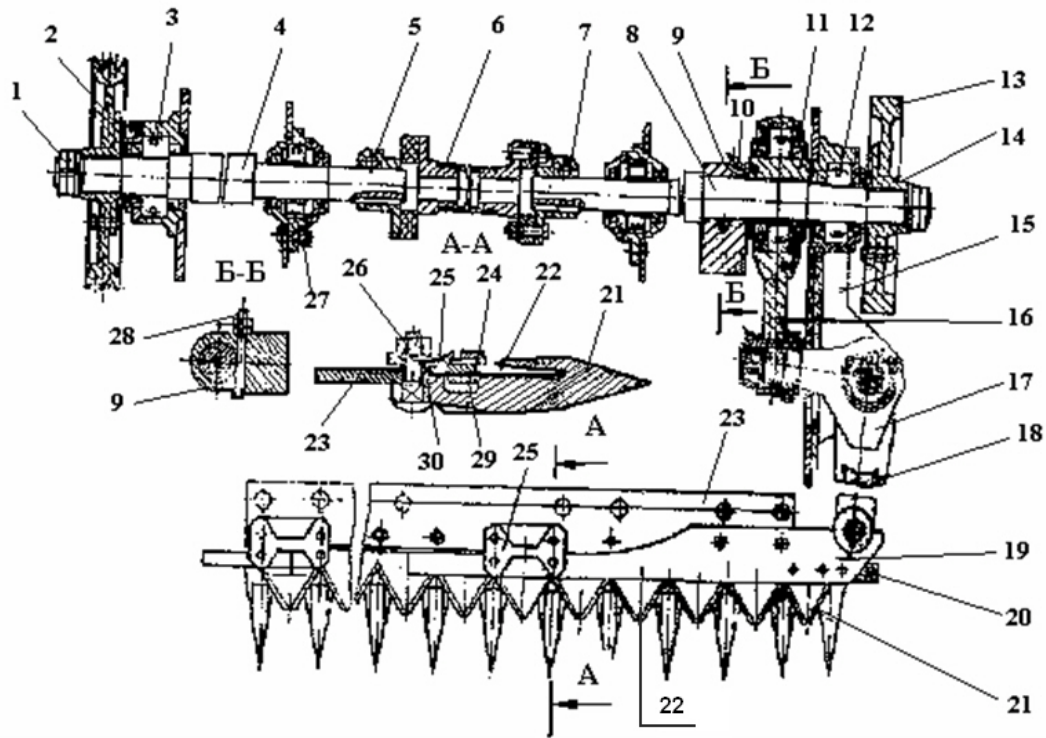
Режущий аппарат и его эксцентриково-шатунный привод с коромыслом:
